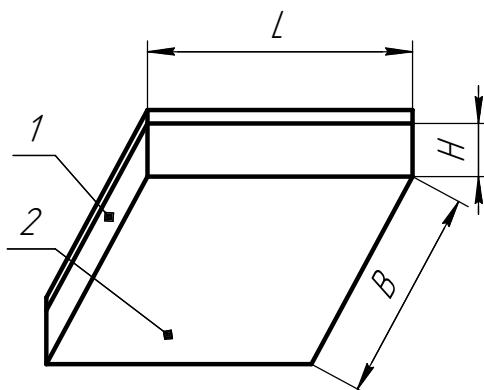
ЛПО46-4x18; 1. Корпус в сборе, 2. Рассеиватель
